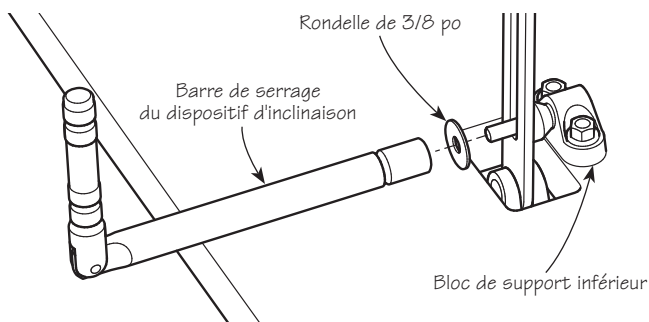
Pose de la barre de serrage du dispositif d'inclinaison
